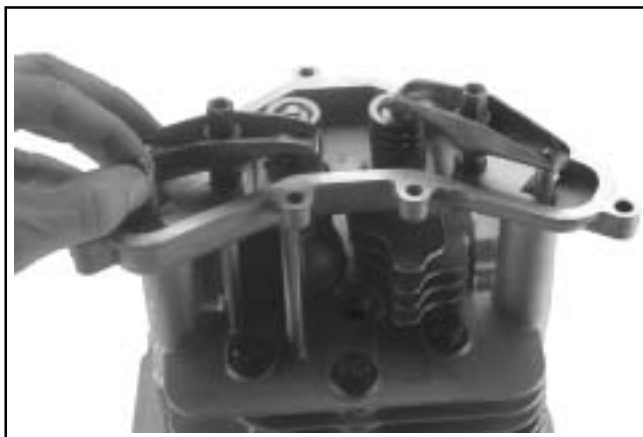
Instalación de los conjuntos de varillas de empuje y balancín.
